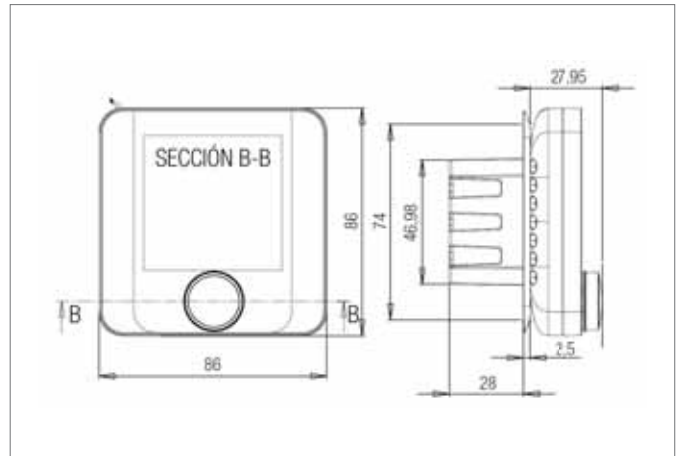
Dimensiones de la HC BUS Room Unit
